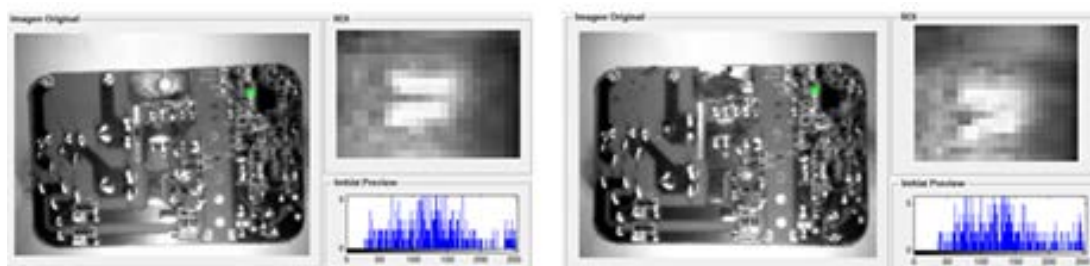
Detección de soldadura excesiva sobre una región.
